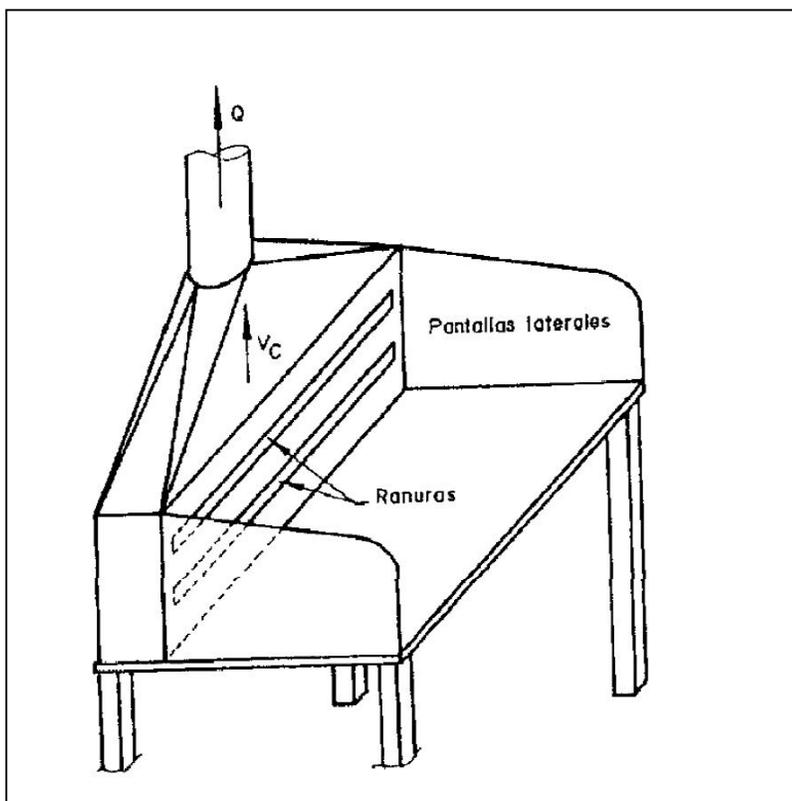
, ventilación para soldadura sobre banco fijo.
